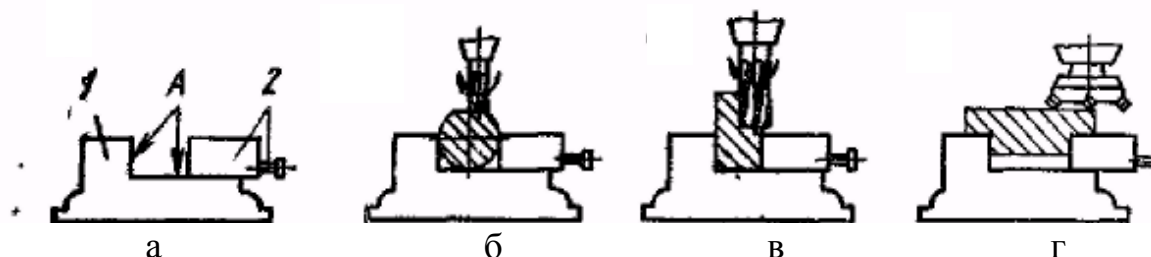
Схема универсально-безналадочного приспособления (а) и его использование при фрезеровании: лыски на валике (б); уступа (в); плоскости (г).
